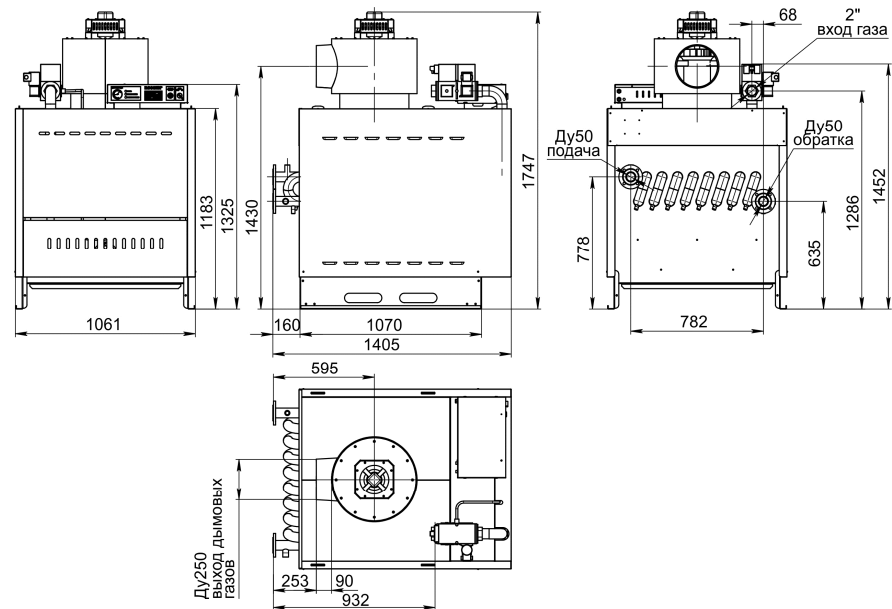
Габаритно-присоединительные размеры RSA300 с дымососом
